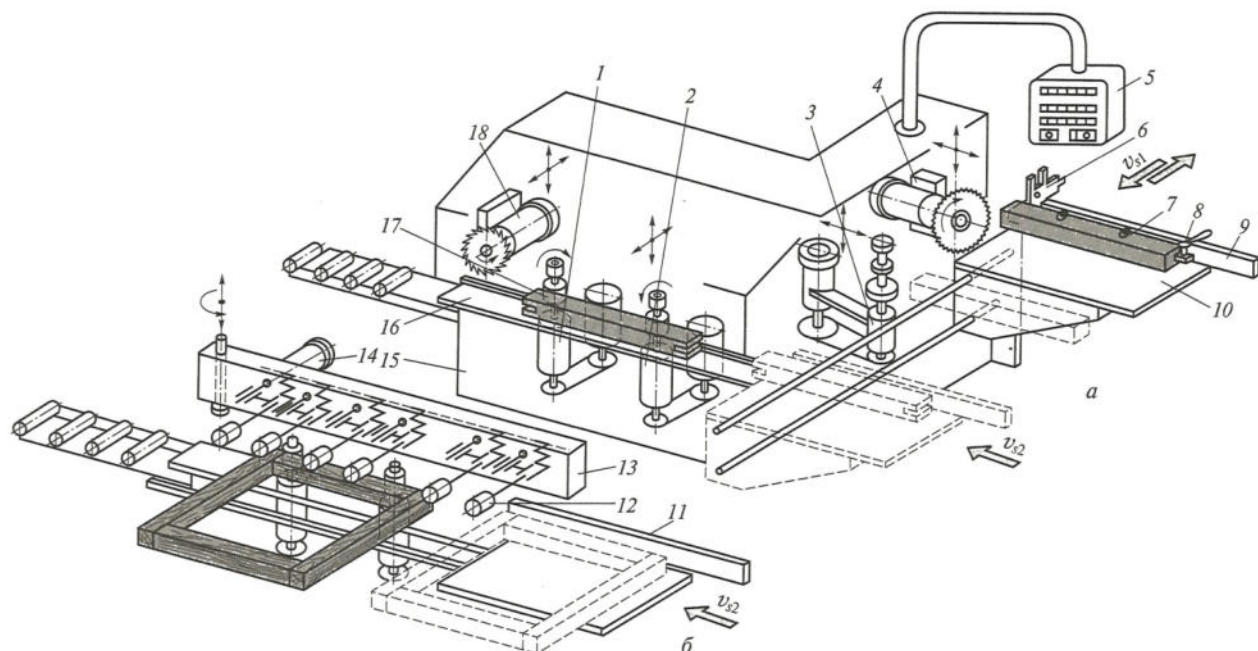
Многоцелевой деревообрабатывающий станок для изготовления окон:
